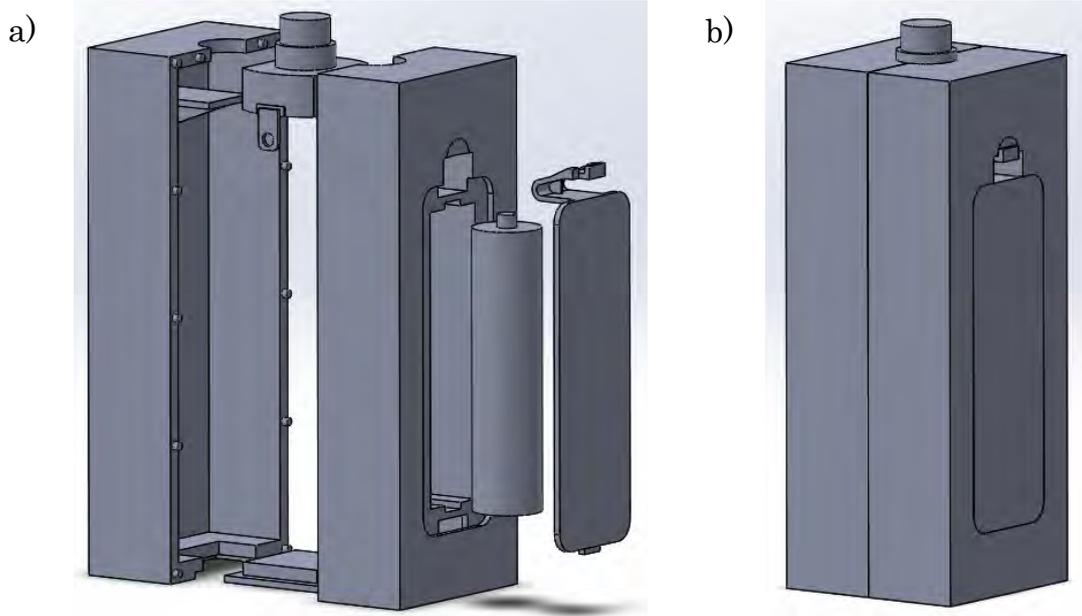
Linterna estilo geométrico, a) vista explosionada, b) vista de conjunto.
